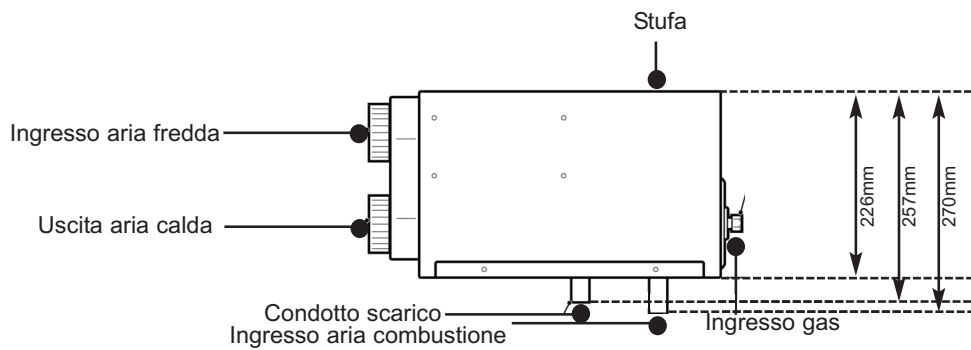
Installazione all'interno – Vista laterale - SH2202 o SC2202
